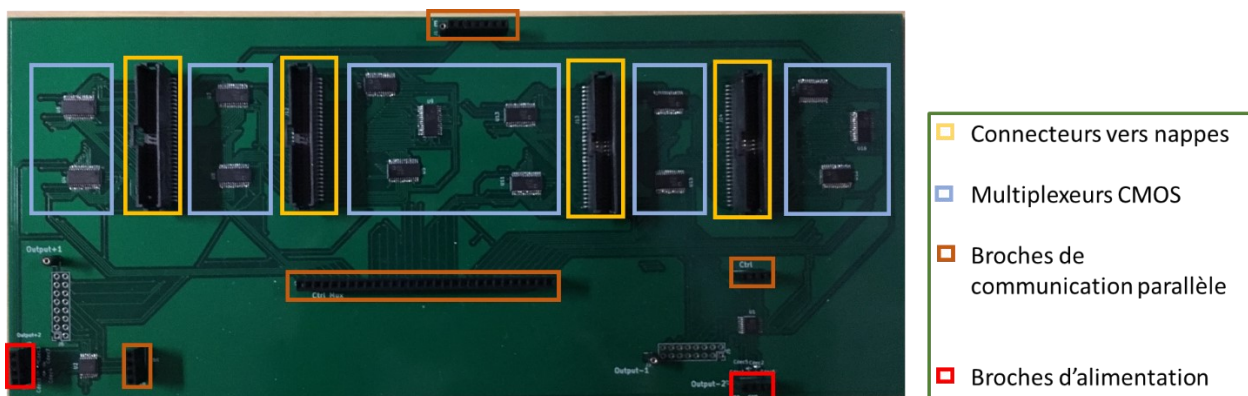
Photo du PCB indépendant servant au multiplexage.
